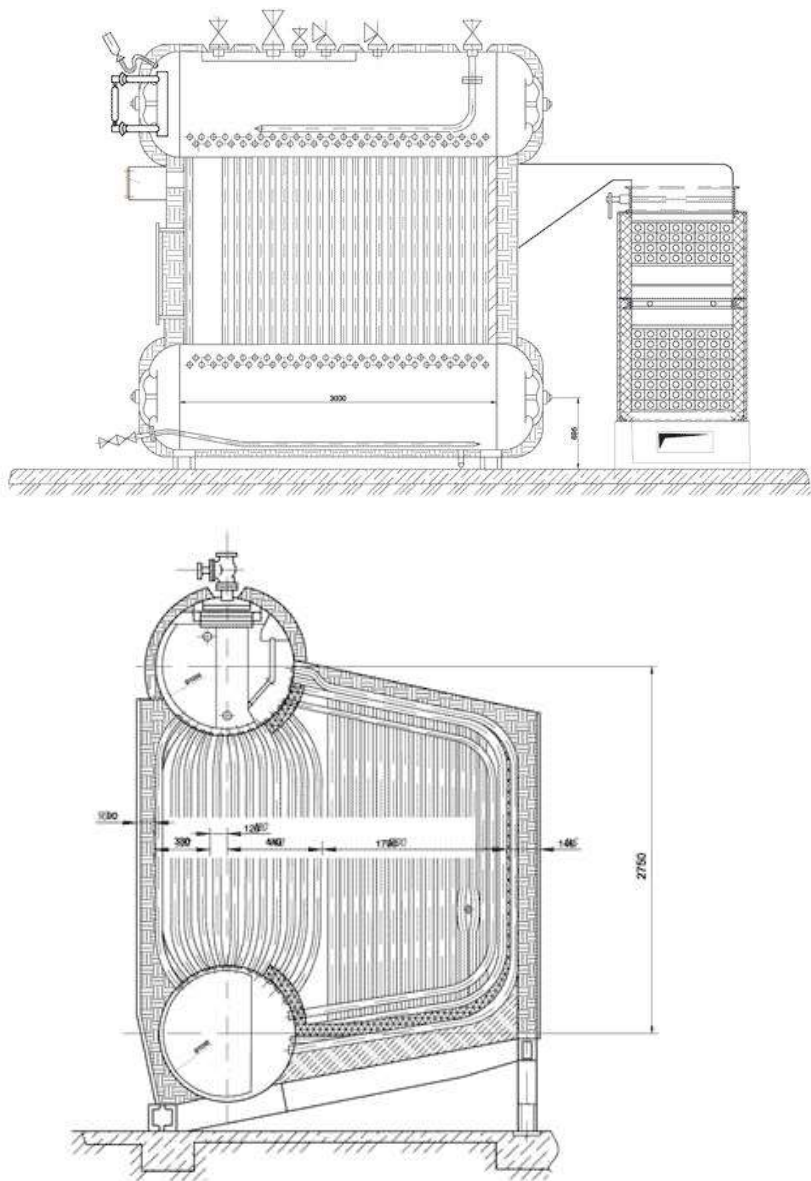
Газомасляный котельный агрегат типа ДЕ-10-14ГМ
